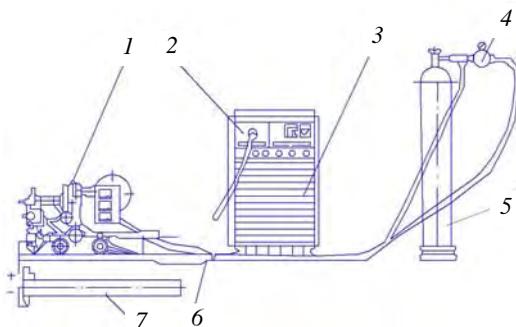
Схема установки для дуговой наплавки в среде углекислого газа:
